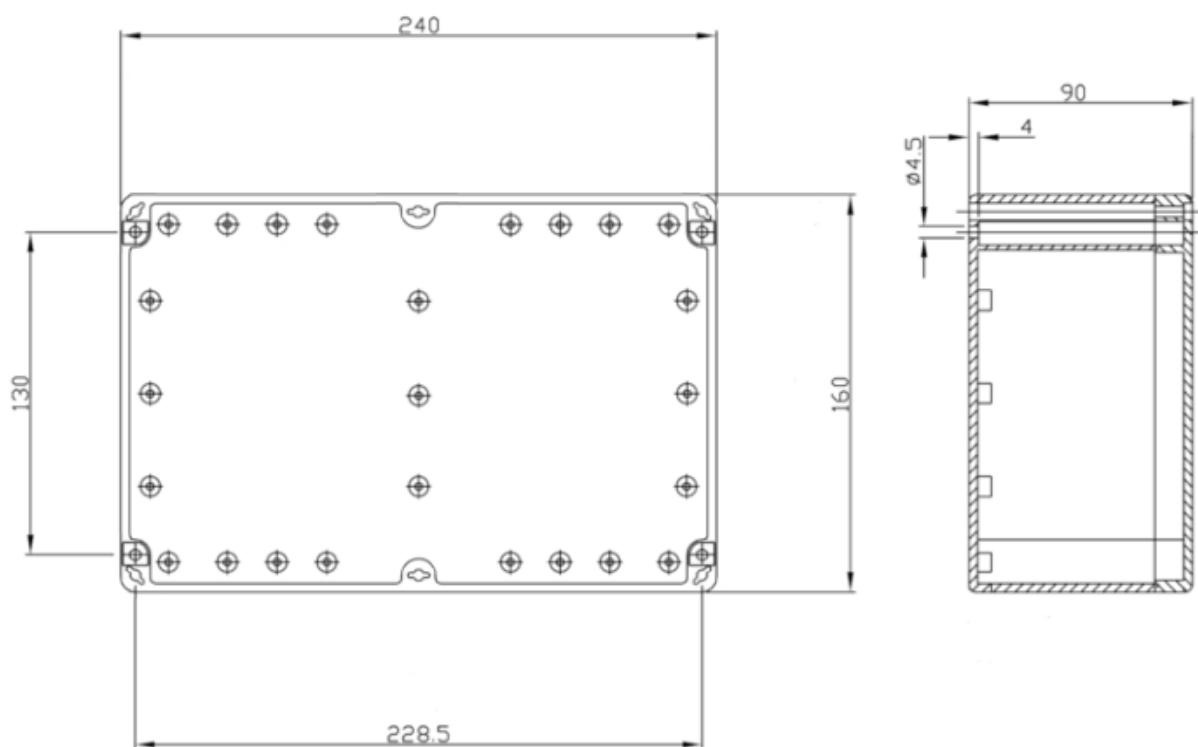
Габаритно-монтажные размеры корпуса контроллера «Квота-1», «Квота-2»
